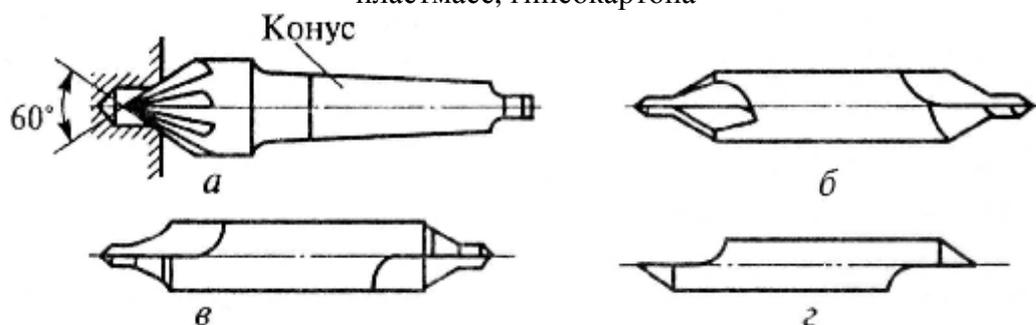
Центровочные сверла: а – многозубая зенковка; б – комбинированное сверло; в – комбинированное сверло с предохранительной фаской; г – однозубая зенковка
